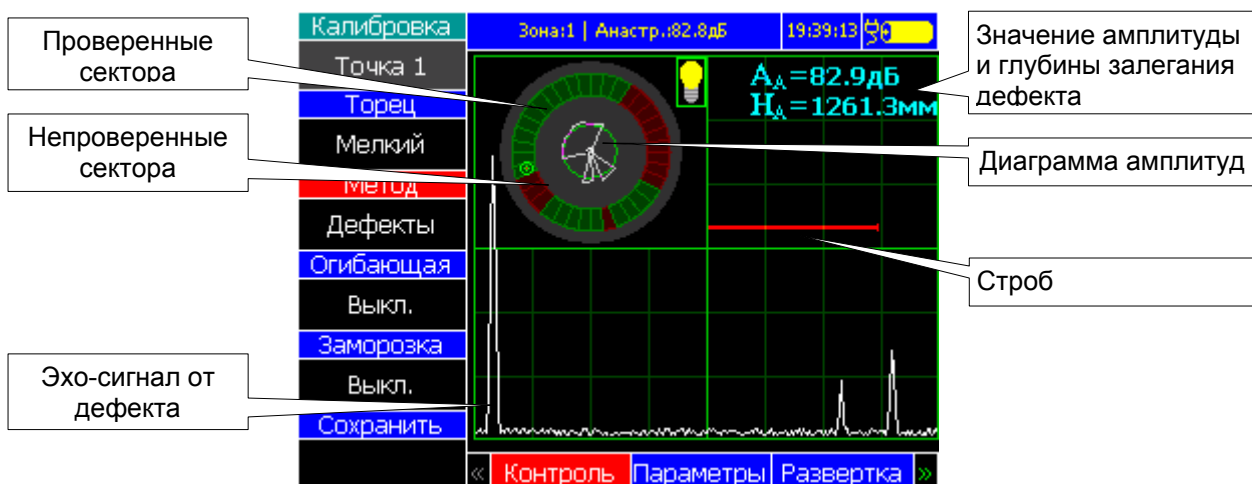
Контроль осевой заготовки на наличие дефектов
